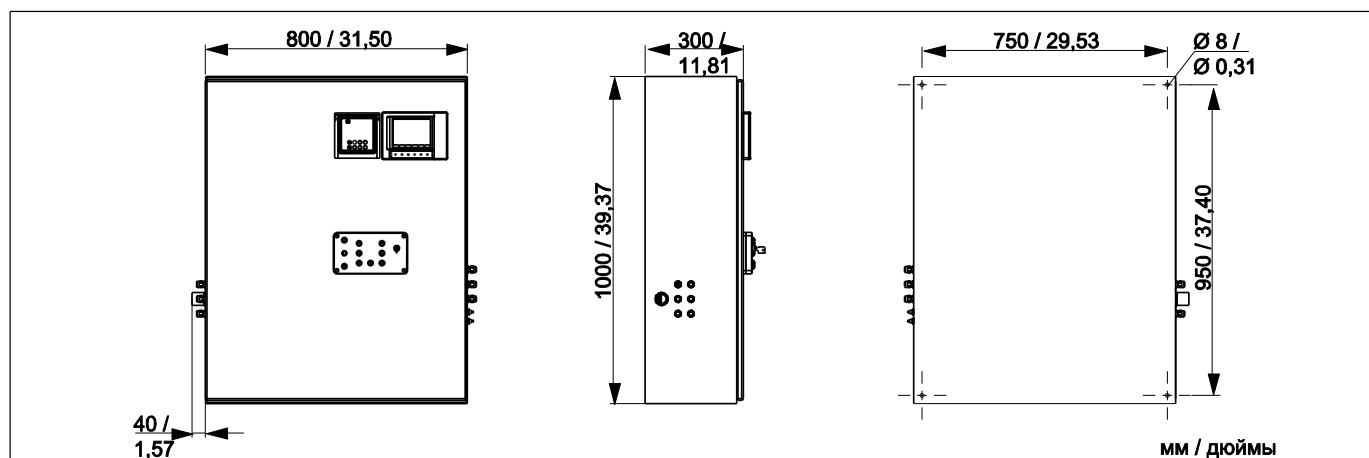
Размеры корпуса CYC300, исполнение из пластмассы
